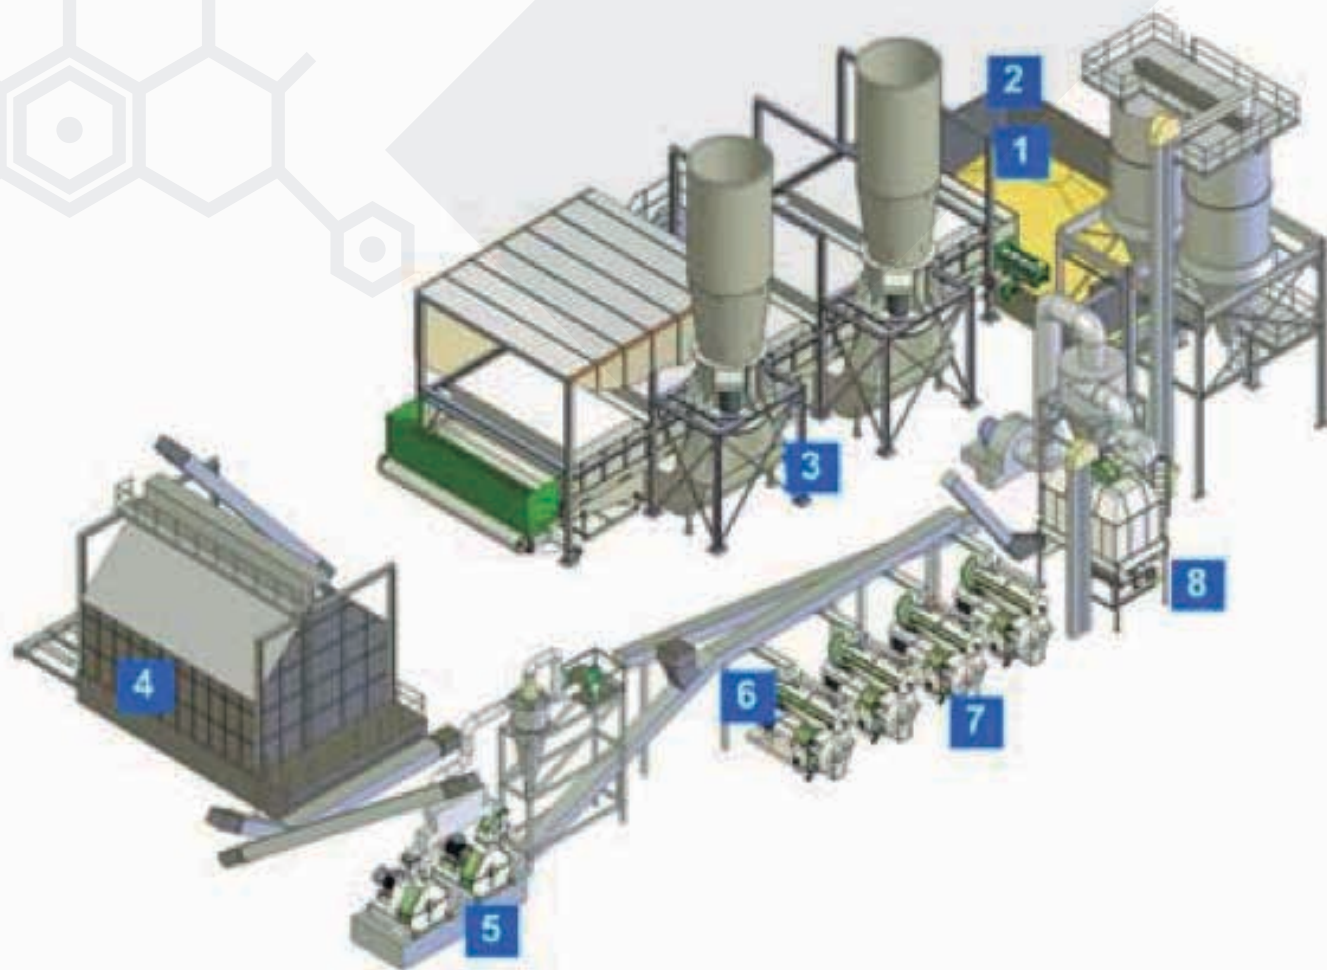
VISTA GENERAL DE UNA PLANTA PELETIZADORA
